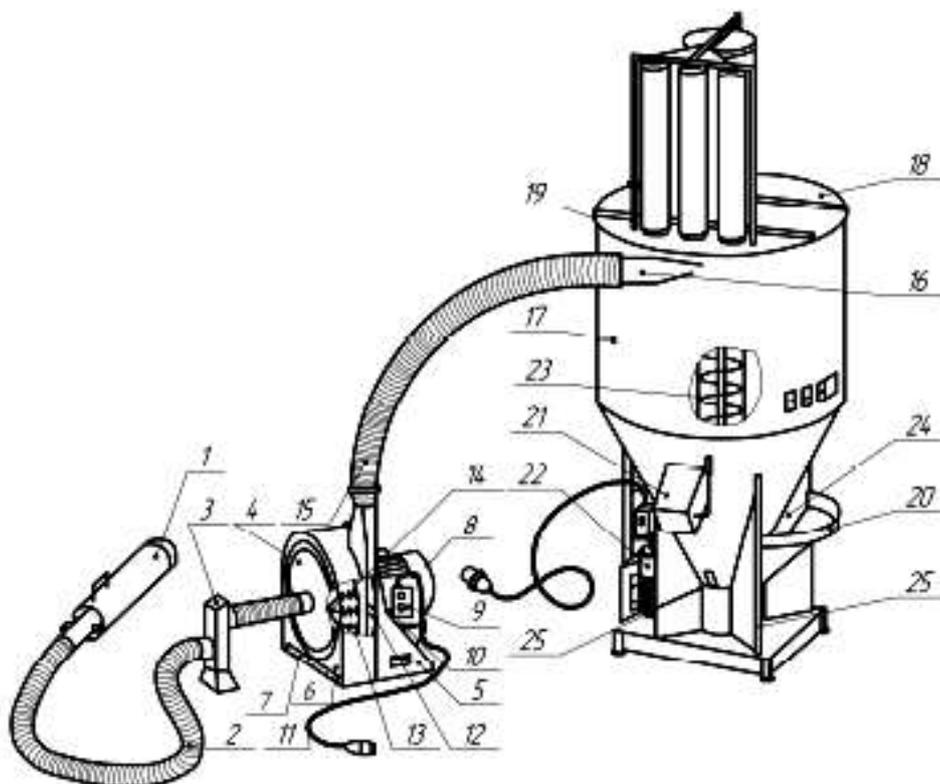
Схема агрегата комбикормового АК-3 «Агрогрант»: 1 – эжектор; 2 – шланг всасывающий; 3 – сепаратор; 4 – шланг соединительный; 5 – станина; 6 – корпус молотковой дробилки; 7 – диафрагма; 8 – электродвигатель; 9 – выключатель; 10 – переключатель; 11 – провод электропитания; 12 – вентилятор; 13 – сито; 14 – ротор ударный; 15 – шланг напорный; 16 – патрубок загрузочный; 17 – смеситель вертикальный; 18 – крышка; 19 – кольцо зажимное; 20 – карман загрузочный для БВМК; 21 – канал разгрузочный для готового продукта; 22 – привод; 23 – шнек-смеситель; 24 – решетка; 25 – отверстие с задвижкой; 26 – система аспирации (фильтры)
